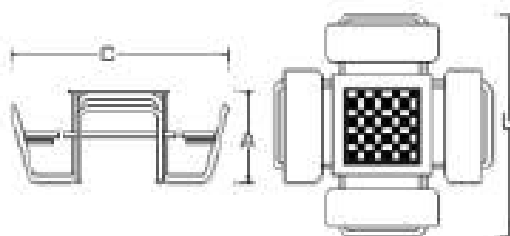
Croquis de Mesas de ajedrez y parchís. (Fuente: <http://www.bricantel.pt/es/>)
